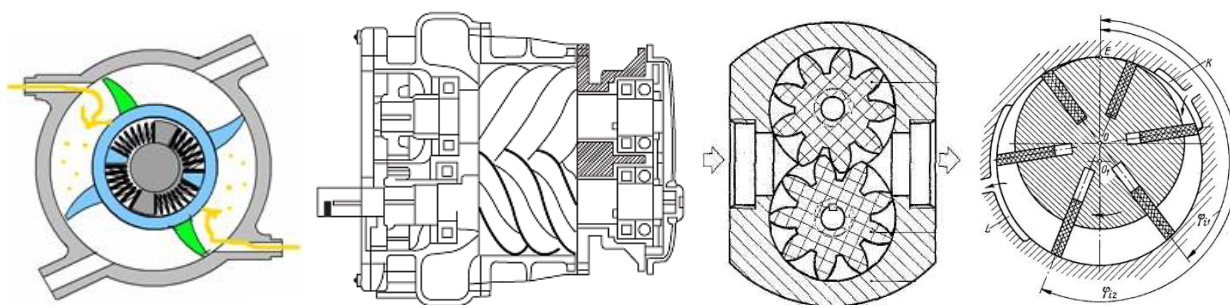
Разрез детандеров объемного типа (слева – направо): лопастного, винтового, шестеренного и пластинчатого
